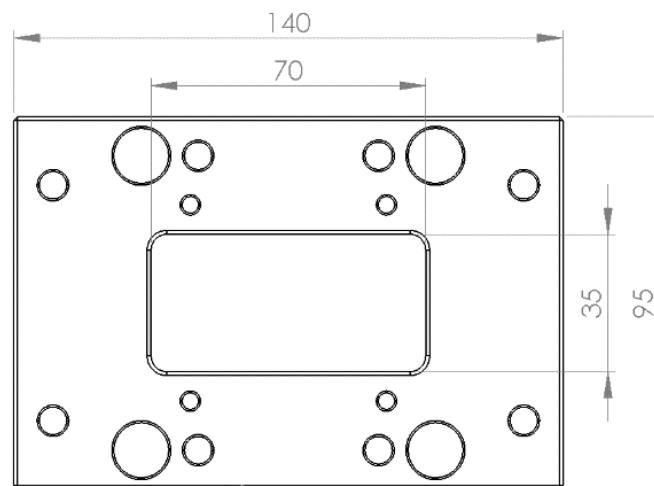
Vista en planta de la placa base (Font pròpia)
